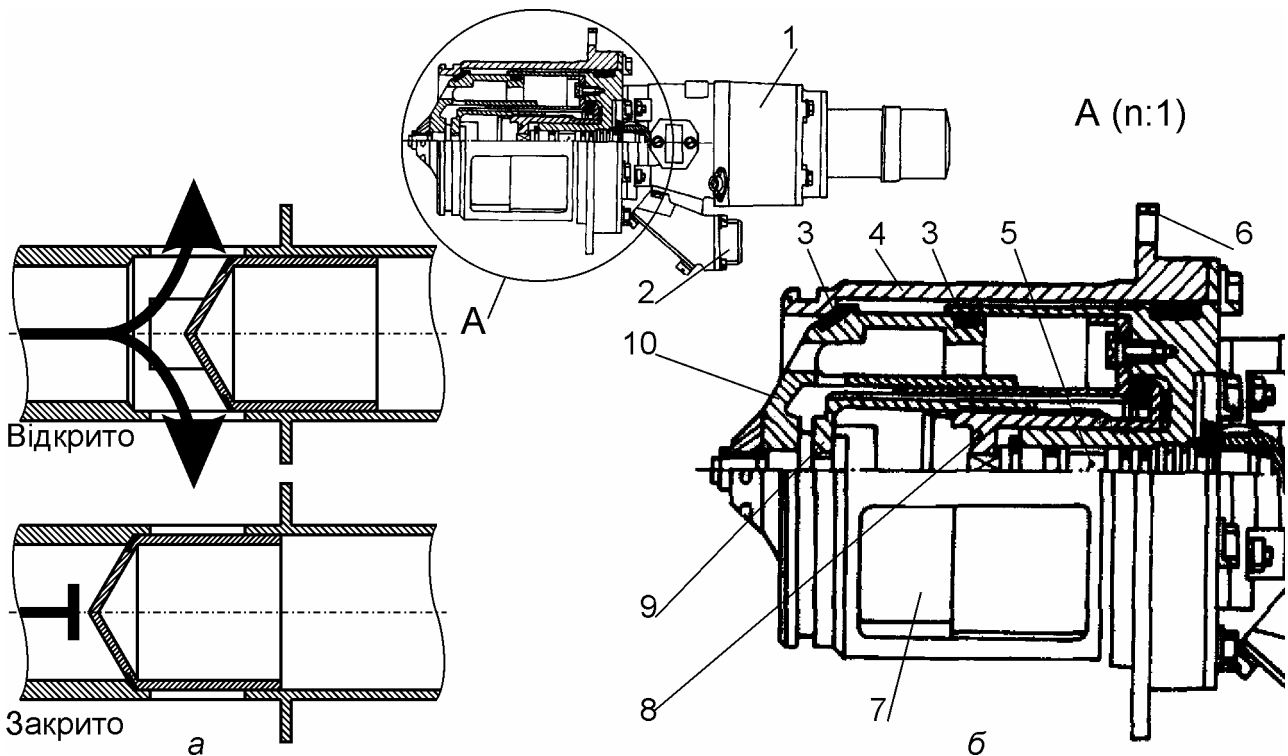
Поршневий кран 772200: а — схема роботи; б — конструкція; 1 — електромеханізм; 2 — електрорознім; 3 — ущільнення; 4 — корпус; 5 — вал; 6 — кріпильний фланець; 7 — вхідне вікно; 8 — ходовий гвинт; 9 — ходова гайка; 10 — поршень
